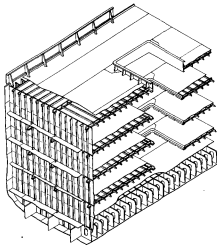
Общий вид и конструкция поперечной переборки многопалубного рефрижератора
